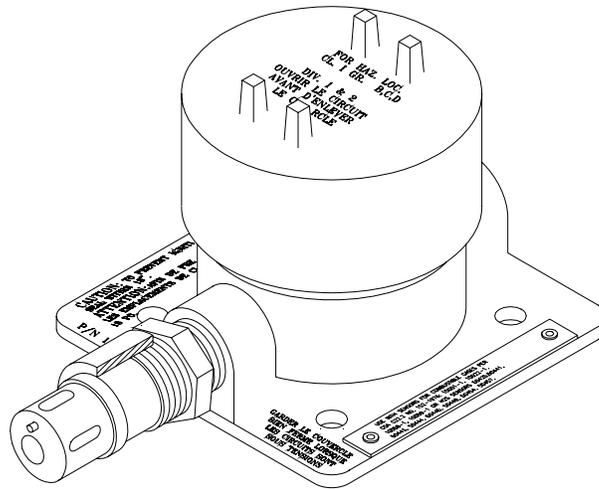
Universal - Sensorgehäuse mit Sensor und Spritzschutz
